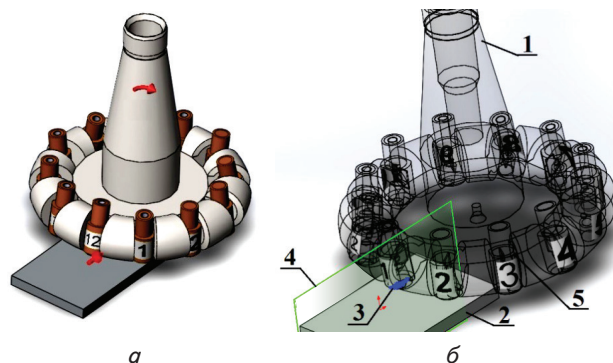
Твердотіла збірна модель фрези та заготовки: а – загальний вигляд імітаційної моделі; б – ескіз моделі в контексті збірки: 1 – фреза; 2 – заготовка; 3 – ескіз з проекцій різальних кромок; 4 – допоміжна площина; 5 – ніж фрези з індивідуальним номером
